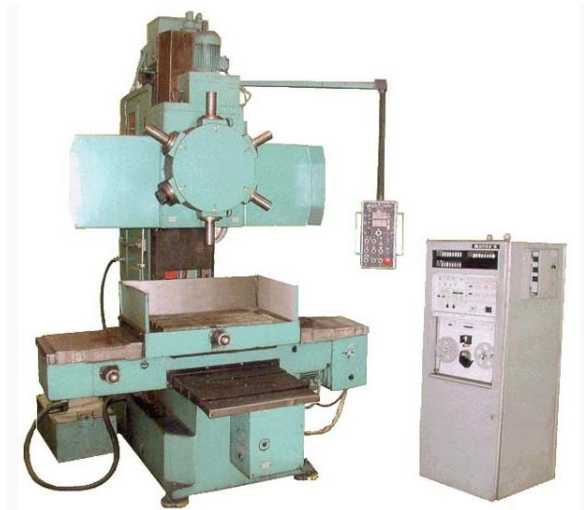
Загальний вигляд верстата 2P135Ф2 – 1
